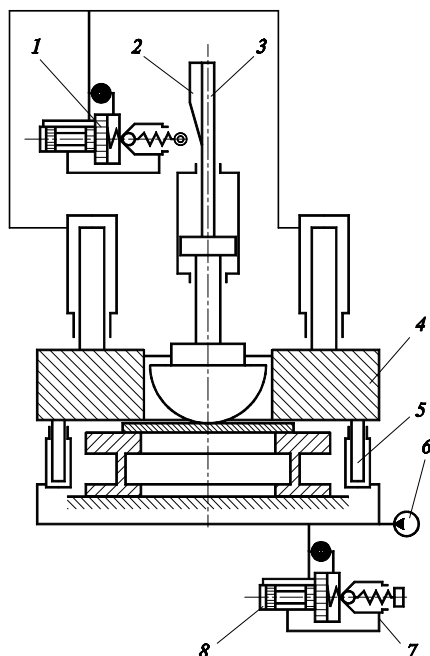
Устройство для штамповки с переменным усилием прижима заготовки
